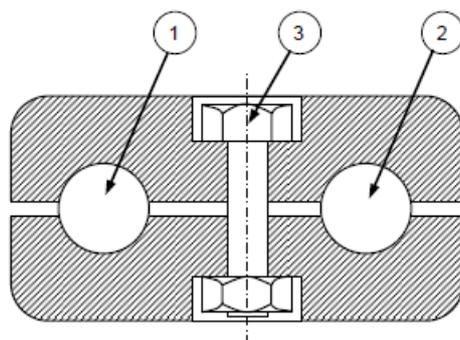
Connessione di un conduttore a sezione circolare ad un ferro d'armatura
